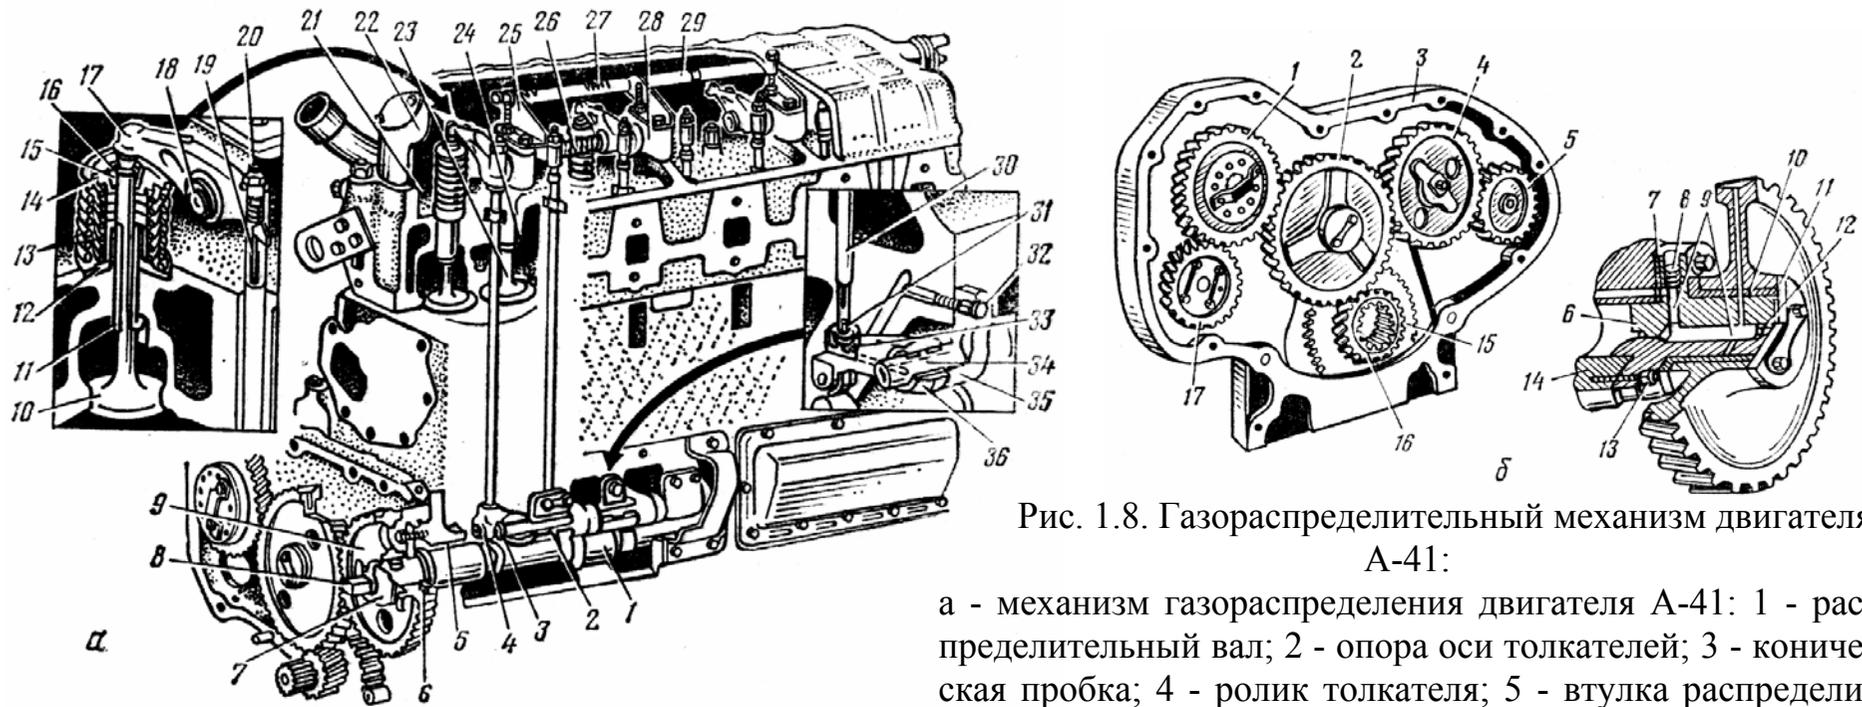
Газораспределительный механизм двигателя А-41:
